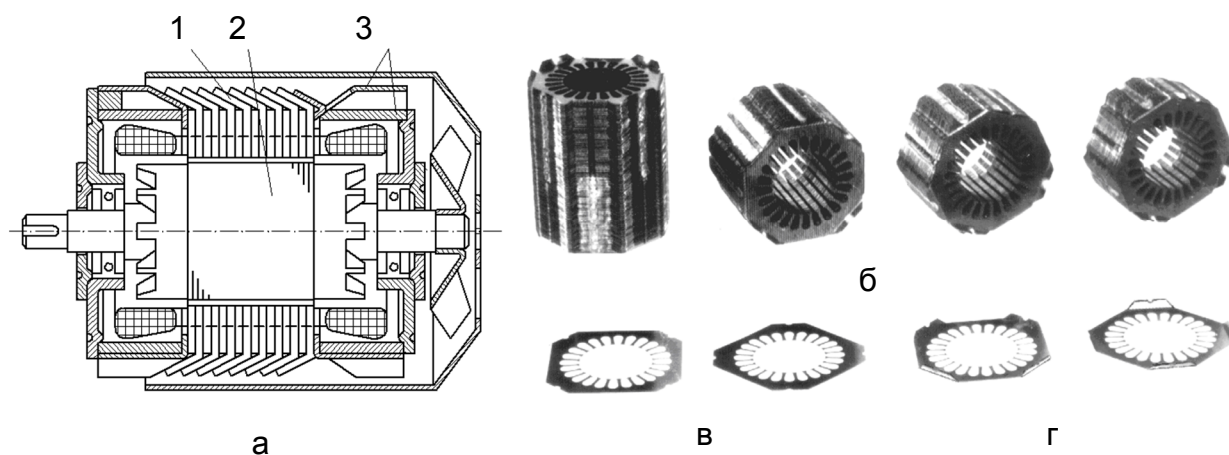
Конструктивна схема закритого безкорпусного асинхронного двигуна (а) з магнітопроводом статора (б), плоскі заготовки (в) і елементарні шари (г) електротехнічної сталі просторової структури: 1 – статор; 2 – ротор; 3 – опорно-стяжний елемент.
